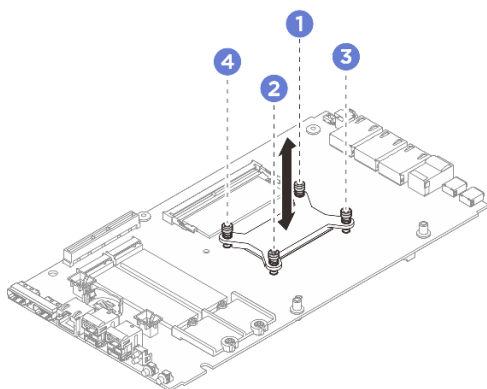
Entfernen des Prozessor-Kühlkörpers
